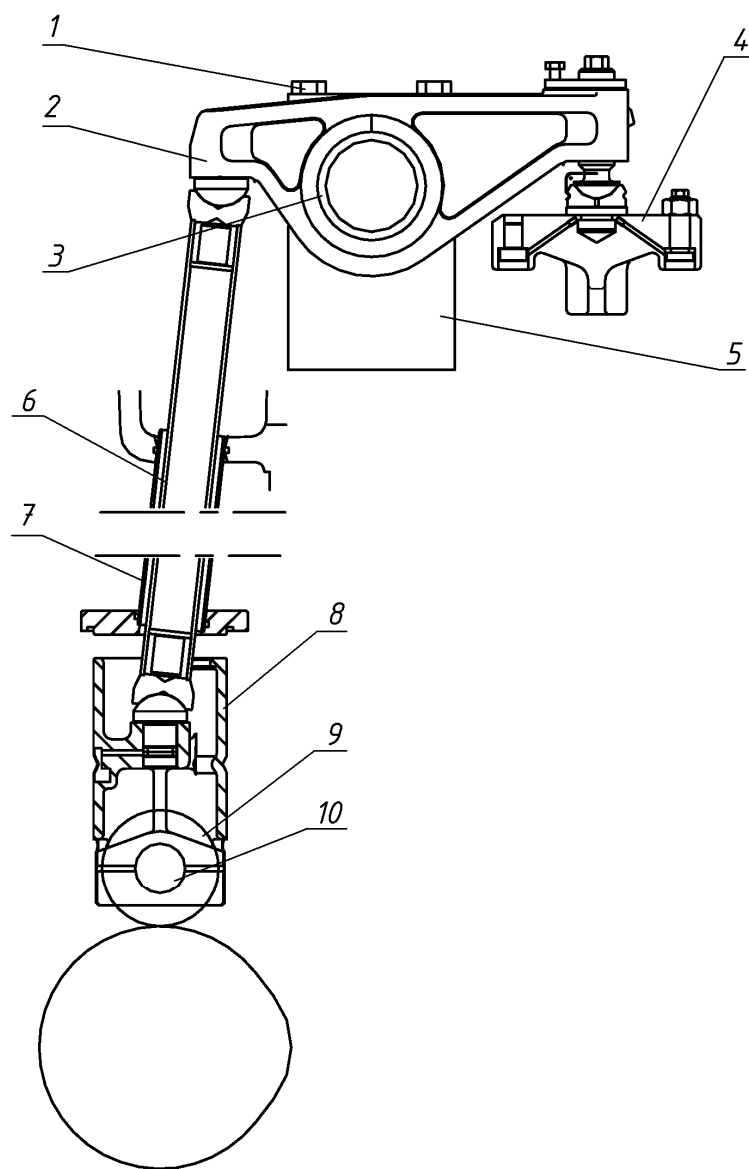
Механізм приводу клапанів газорозподілу: 1 – гвинт; 2 – коромисло; 3 – стопорне кільце; 4 – клапанна траверса; 5 – стійка коромисла; 6 – шток штовхача; 7 – захисна трубка; 8 – напрямний блок; 9 – штовхач клапана; 10 – вісь ролика
